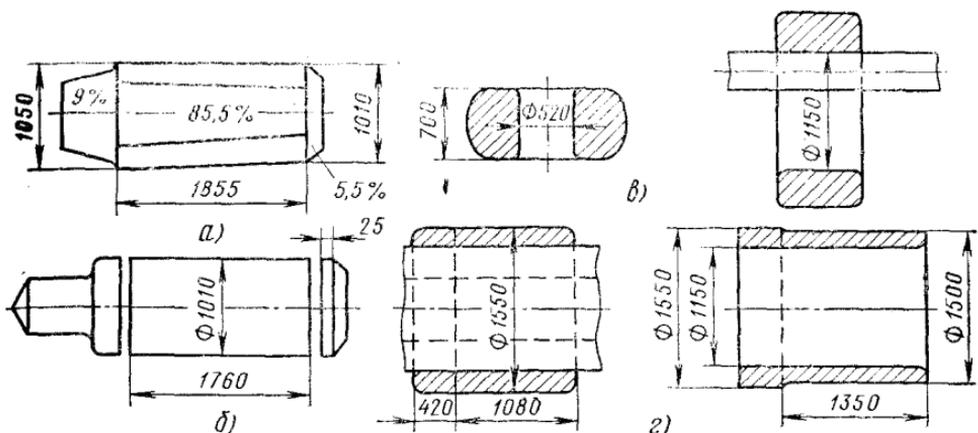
Ковка цилиндра из малоприбыльного слитка
